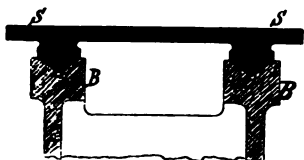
Kraftschlüssige Geradföhrung bei Hobelmaschinen.
